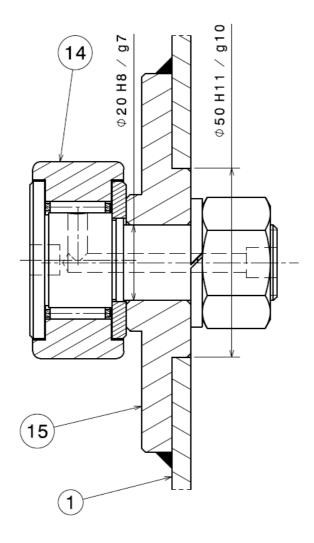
Dessin d'ensemble du montage du galet 14 sur le châssis 1
